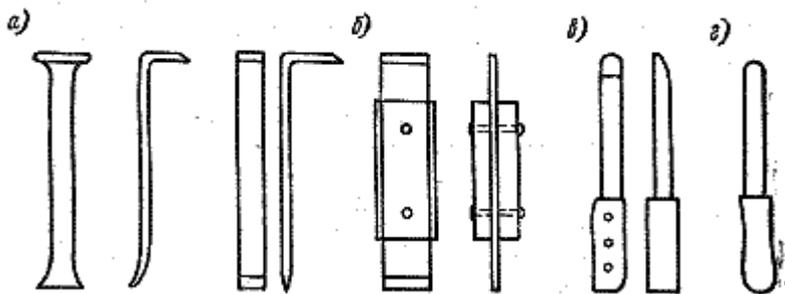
Шкрябки: а — из напильника; б — из ленточной пилы; в — стамеска; г — нож.
